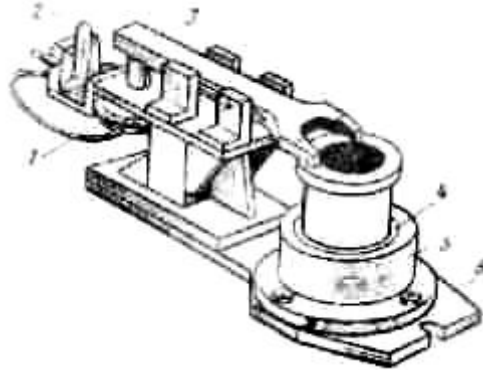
Пристосування для установки і кріплення гільз
